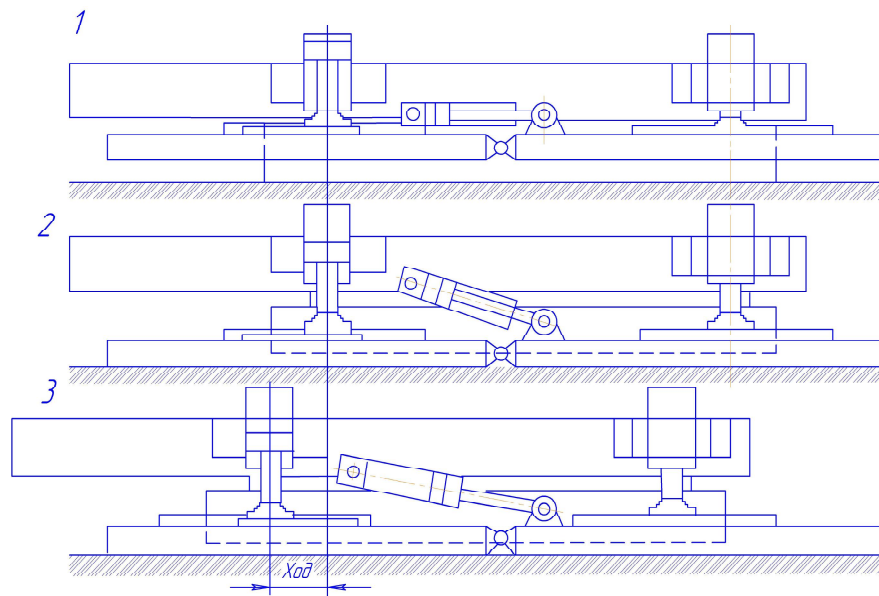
Схема четырехопорного механизма шагания драглайна ЭШ-100.100 с гидроприводом /
